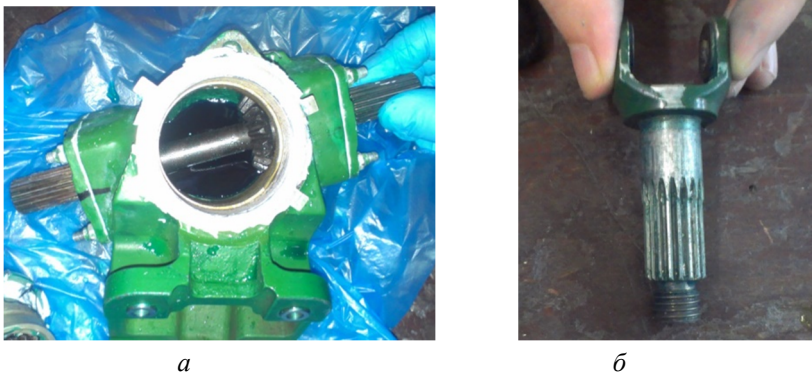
Кутовий редуктор: *a* – корпус редуктора з валом-шестернею, *б* – карданний вал шестерні 5
